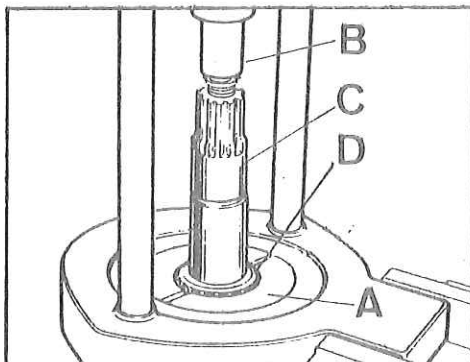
Desmontaje del cojinete de cabeza del piñón de ataque
